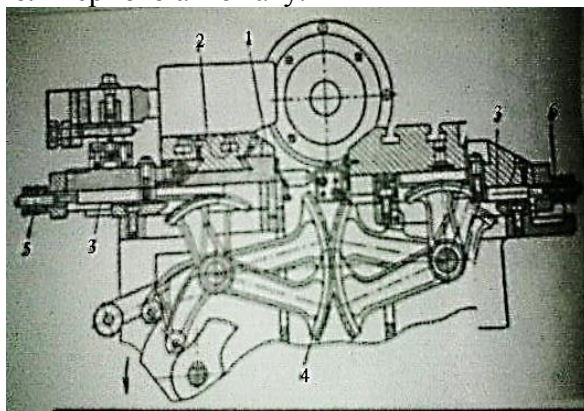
Поперечні супорти токарно – револьверного автомату
